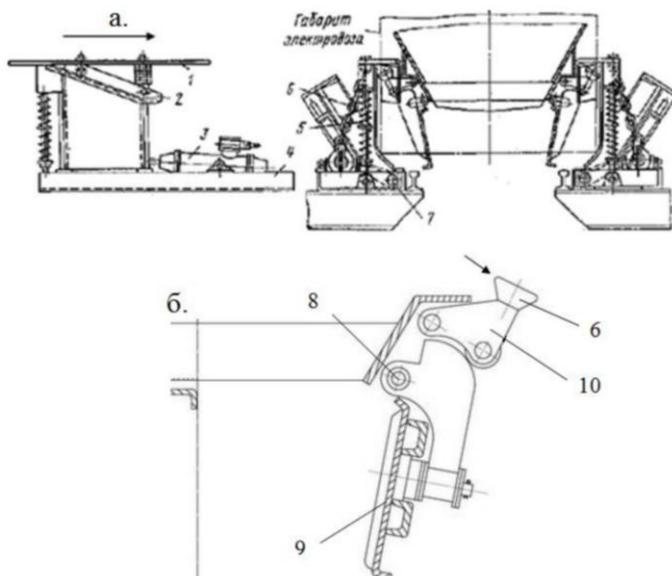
Устройство для закрывания днищ (клапанов): а – общий вид, б – положение роликового замкового устройства при открытом днище.
